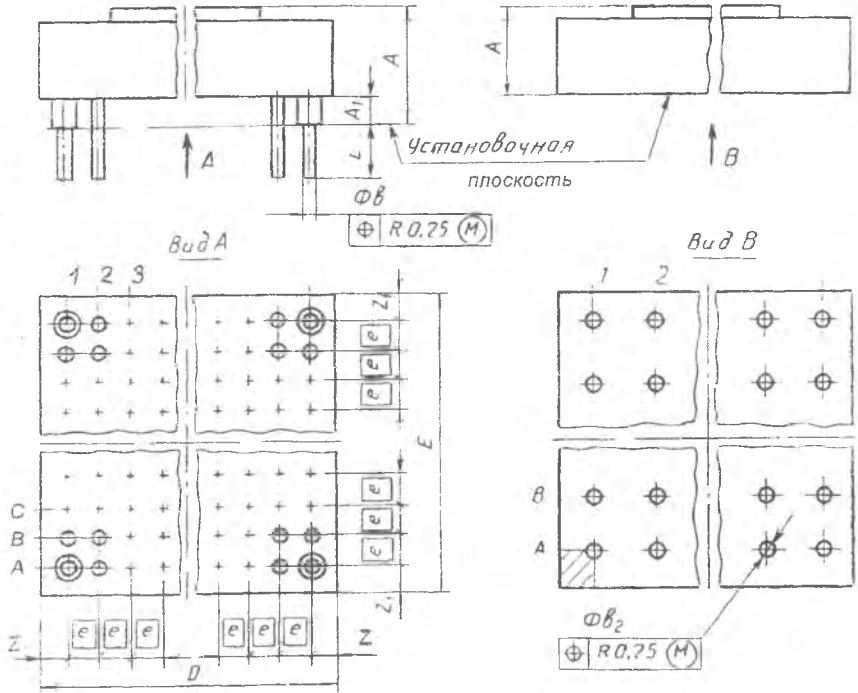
Конструкция корпуса типа 6 подтипа 1
